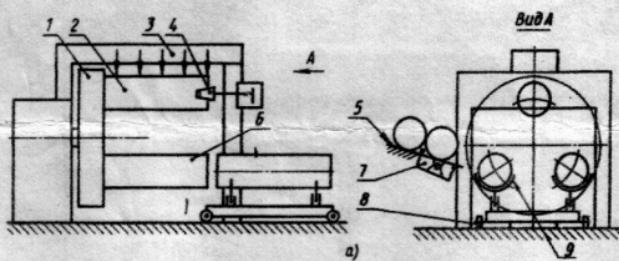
Полуавтоматическая установка для сборки и сварки продольных швов обечайек
